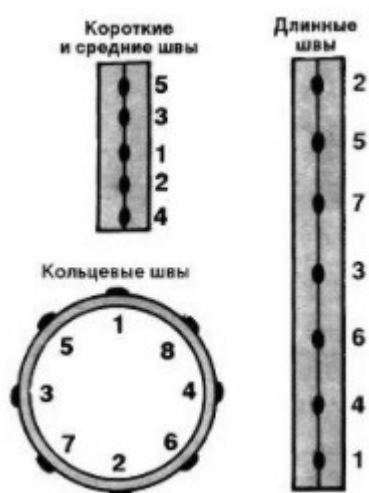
Порядок постановки сварочных прихваток
